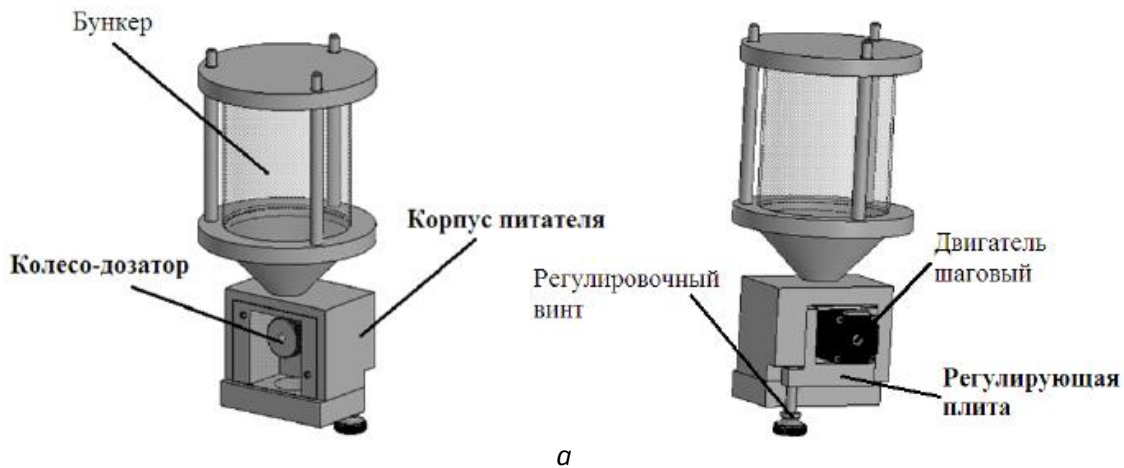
Модернизированный порошковый питатель для плазменно-порошковой наплавки:
